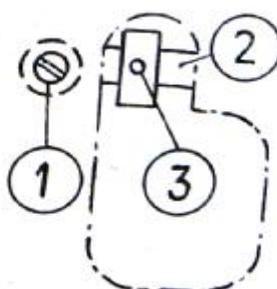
Регулировка угла наклона переднего двигателя ткани
